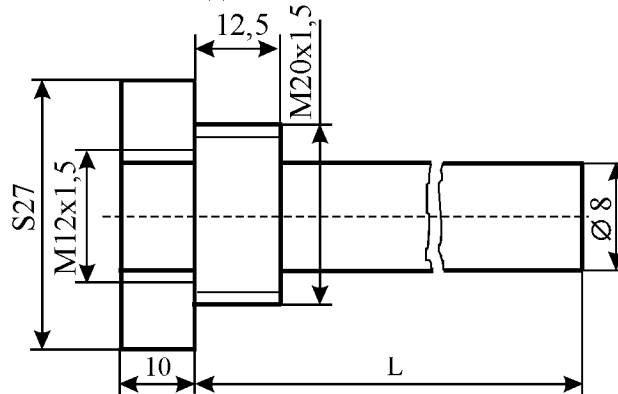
Габаритные и установочные размеры измерительного блока
